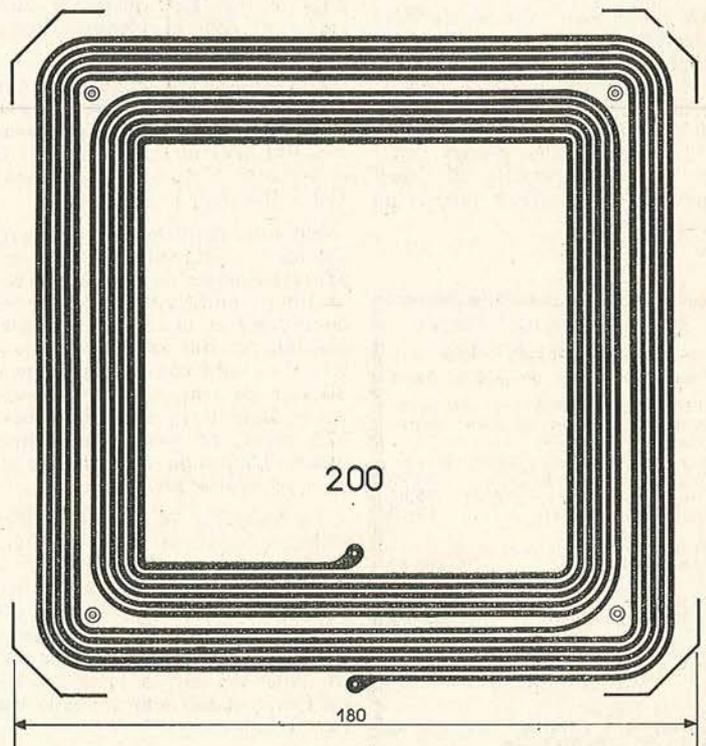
Le bobinage à circuit imprimé de la sonde exploratrice (échelle 1/2)
